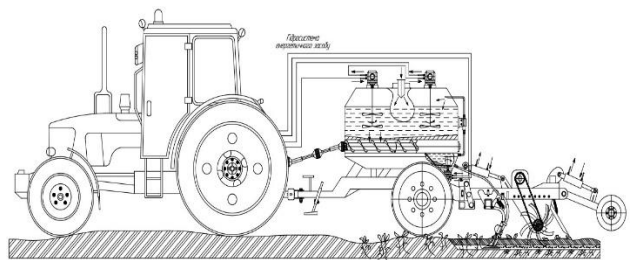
Загальний вигляд машинно-тракторного агрегату для технології Strip-till
